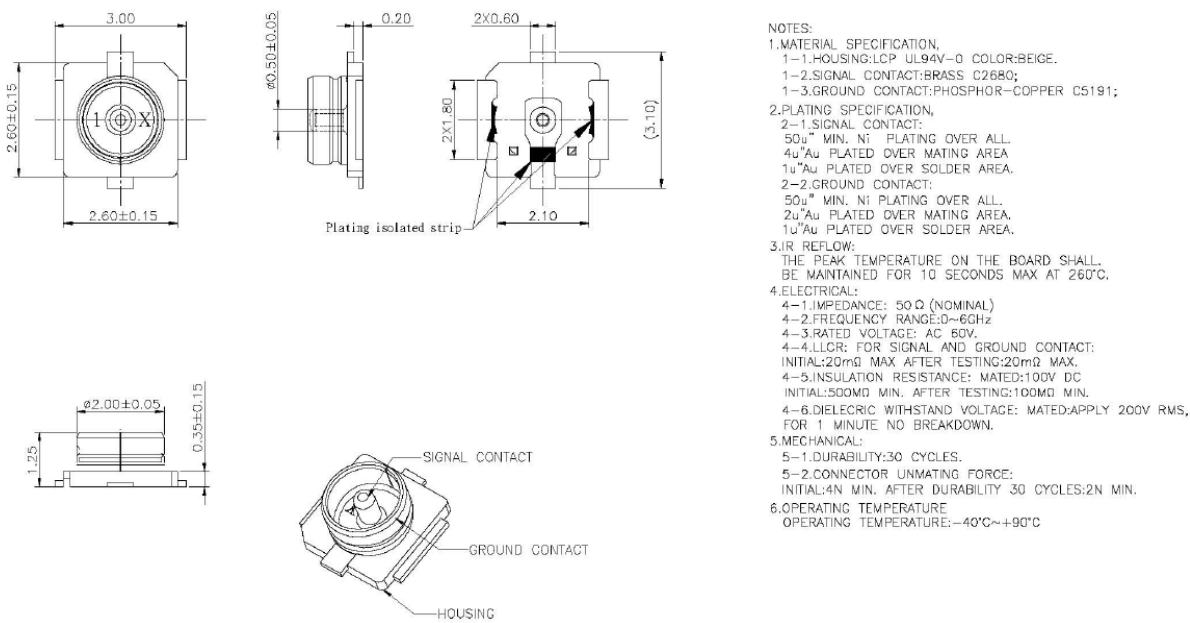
1代 IPEX 焊盘尺寸
